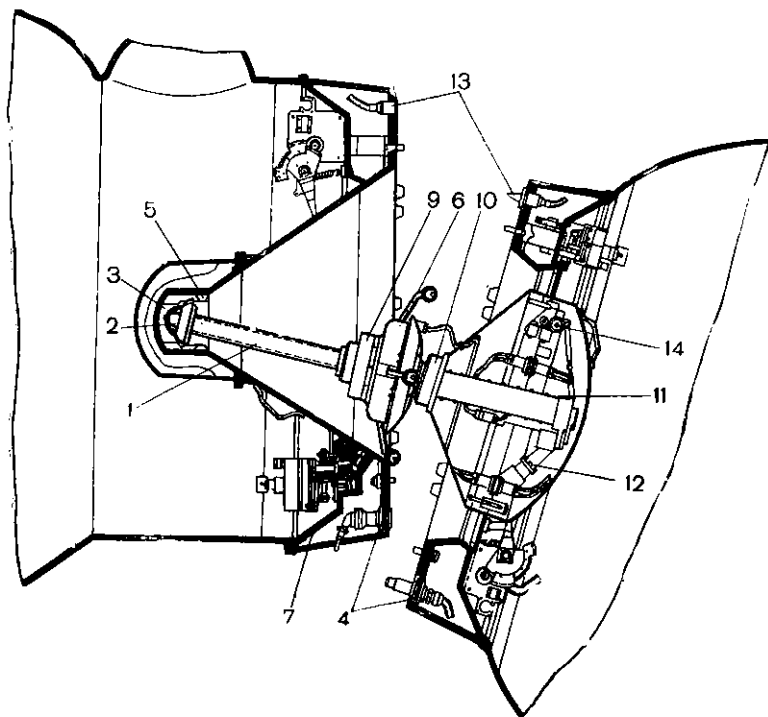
Упрощенный чертеж стыковочного устройства, применявшегося при стыковке кораблей «Союз-11» и станции «Салют». Устройство показано в момент сцепки кораблей.
